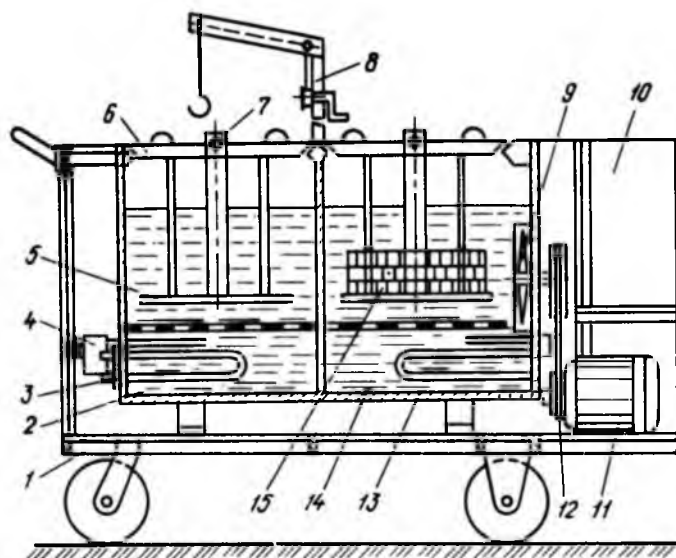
Установка для промывки и проварки втулочно-роликовых цепей:
